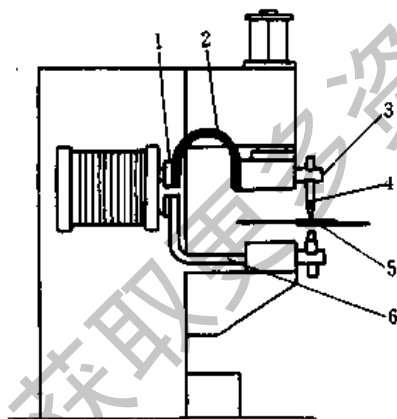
点焊机或凸焊机的焊接回路
